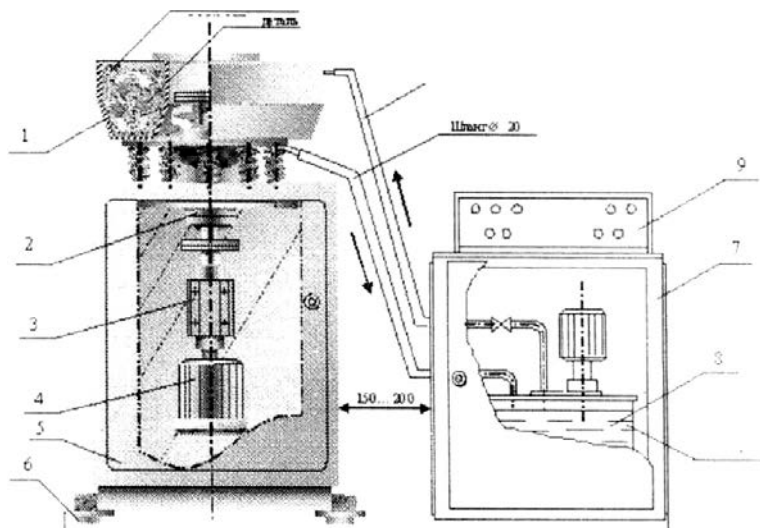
Вибрационный станок с торовой формой рабочей камеры
